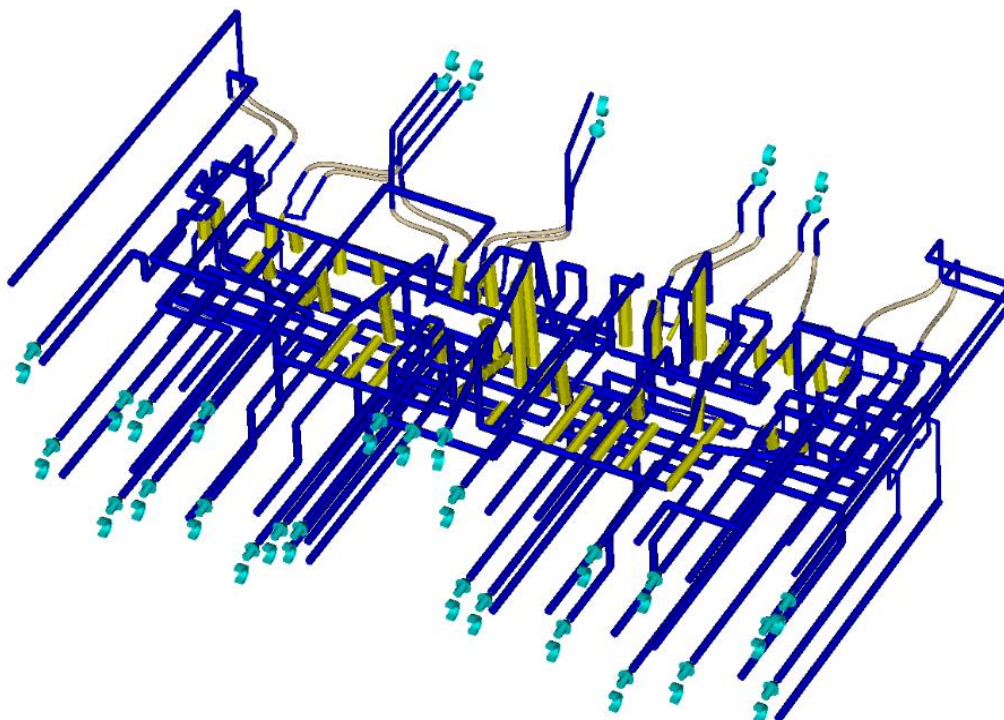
Sistema de arrefecimento utilizado após gerar a malha
